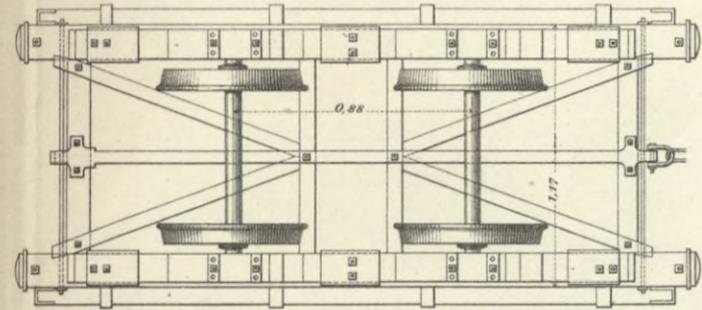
Seitenkipper vom Bau der Berliner-Verbindungsbahn.
